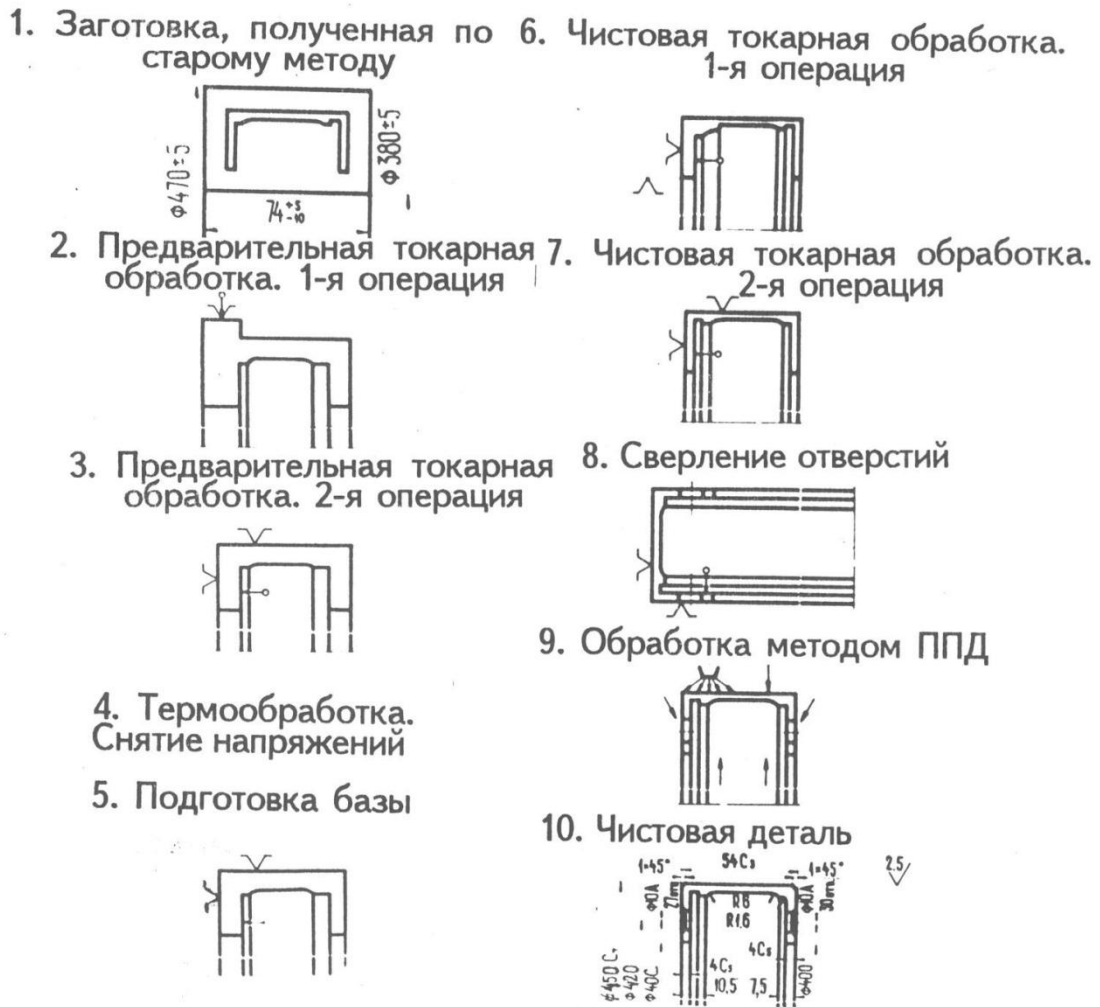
Технологическая схема изготовления промежуточного кольца диска компрессора из сплава ХН68ВМТЮК-ВД:
